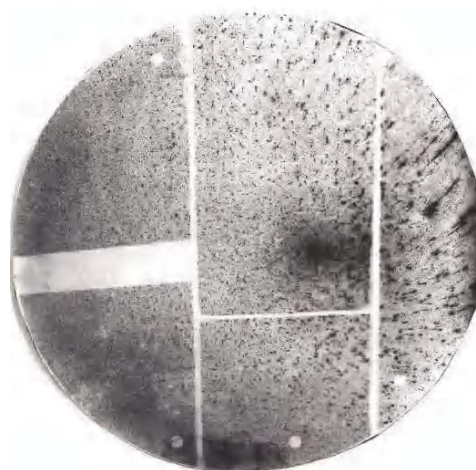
Смещение внеосевой ликвации на цапфе заготовки роторного вала со стороны верха слитка, х 0,4
